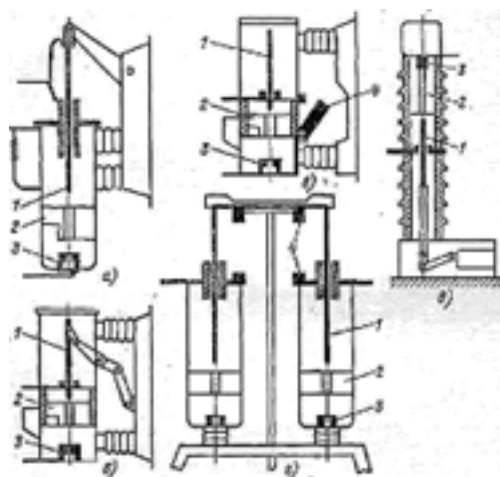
Схемы конструкции выключателей маломасляного типа
